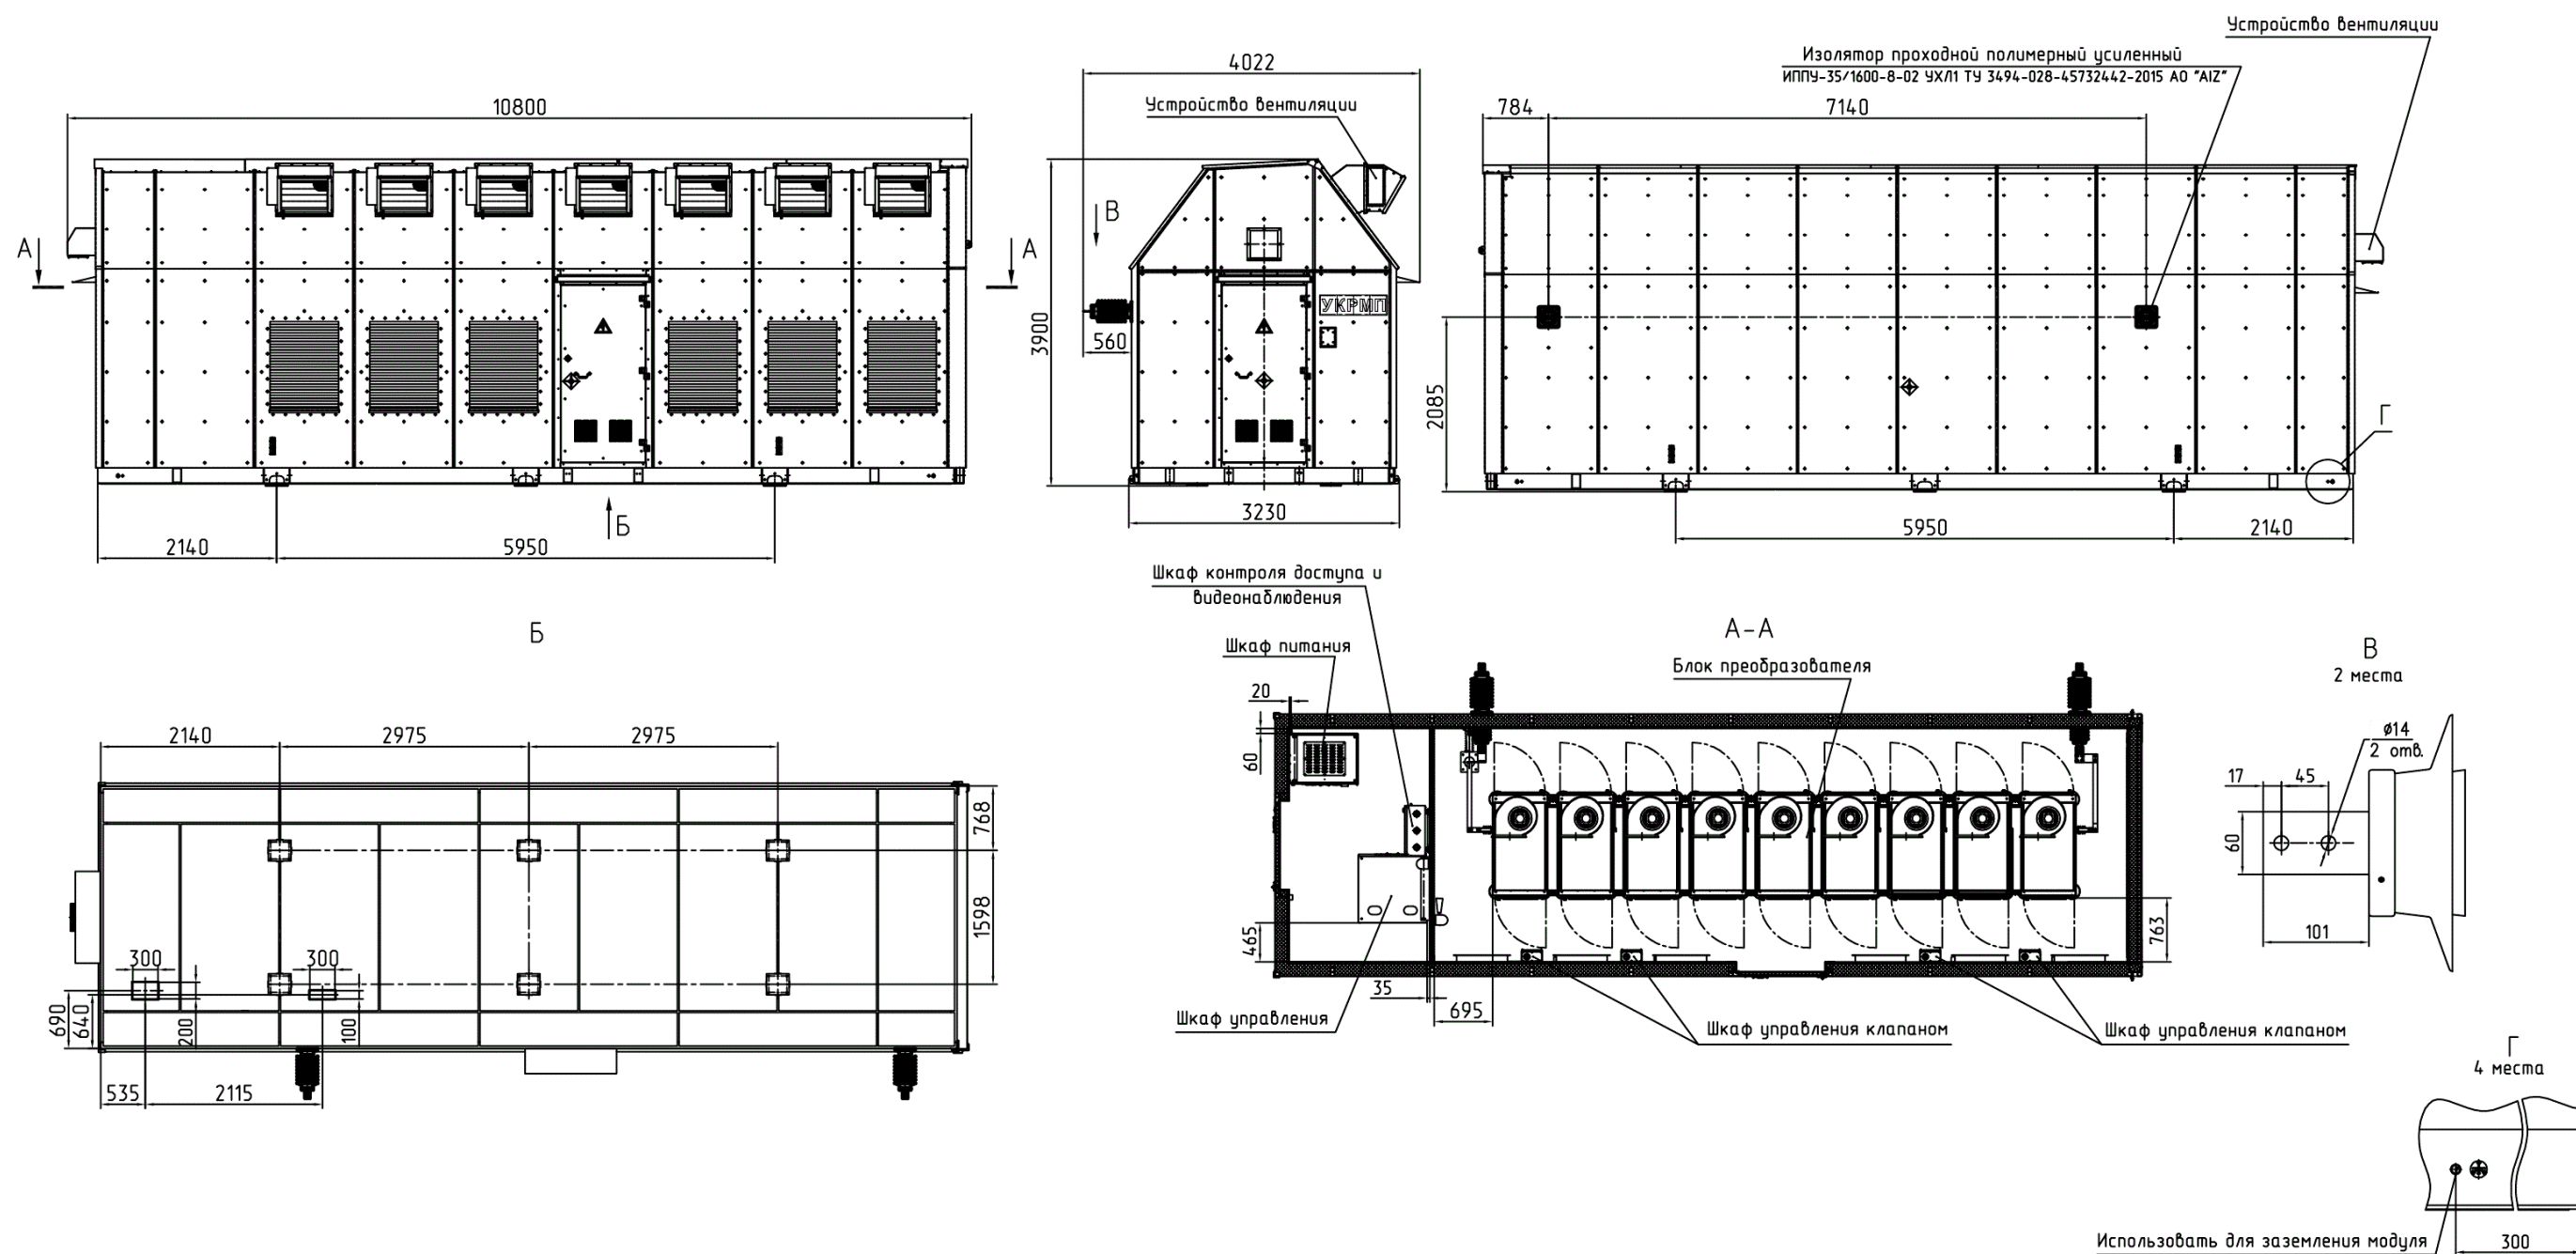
Габаритный чертеж модуля преобразователя УКРМП-27,5 кВ
